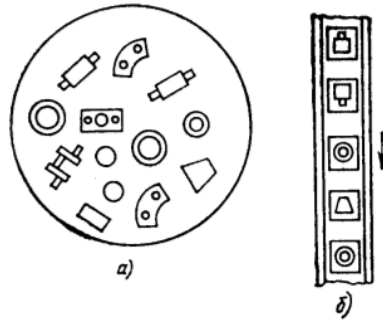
Виды расположений деталей: а) неподвижных; б) перемещающихся
